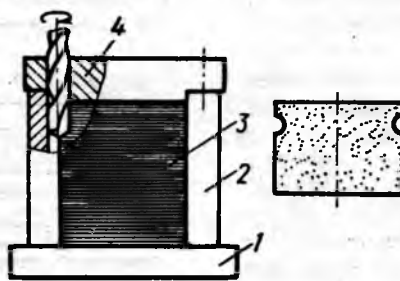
Кондуктор для сверления заплечиков в лепестках
